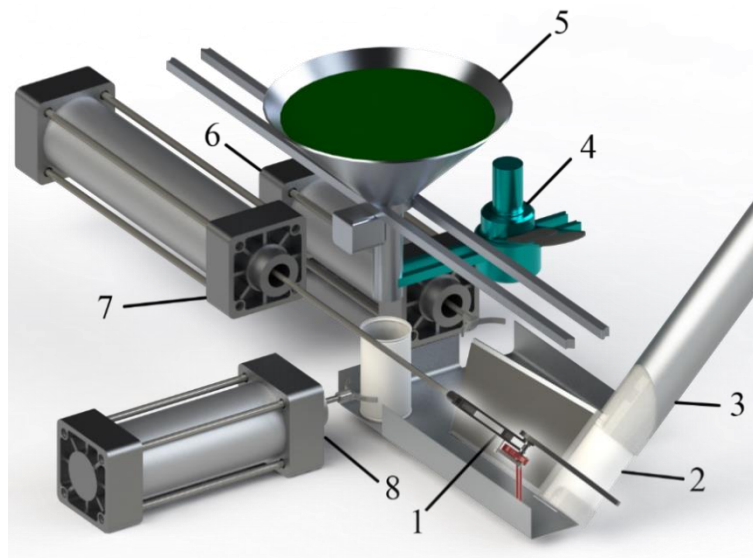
Принципова модель пневматичної системи автоматизованої комірки по заповненню циліндричної тари сипучими продуктами:
